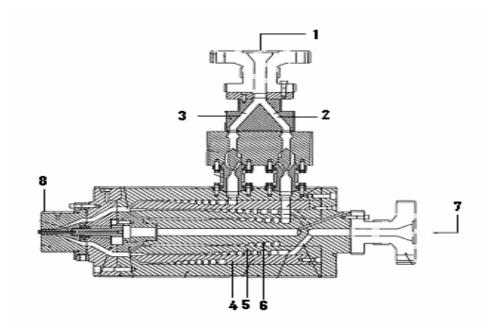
Extrusora doble para recubrimiento de piezas cilíndricas.
